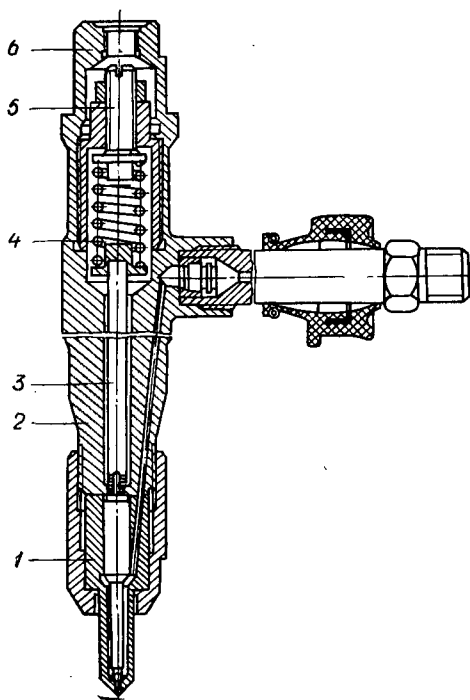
Форсунка двигателя ЯМЗ-236-Н-6:
